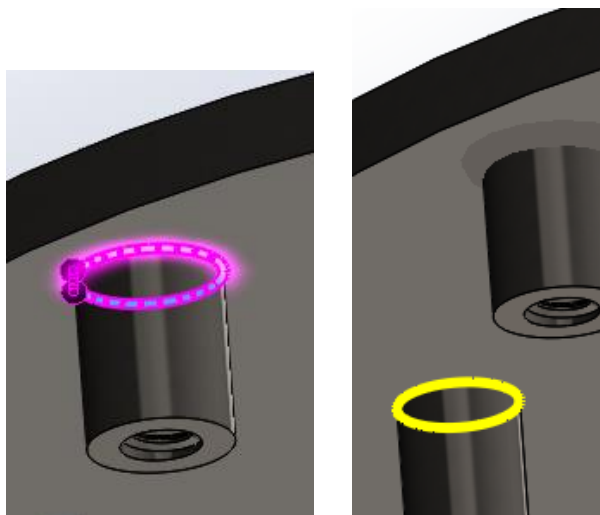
Cordones de soldadura para tuercas remachables y perno en J (Fuente: propia)
